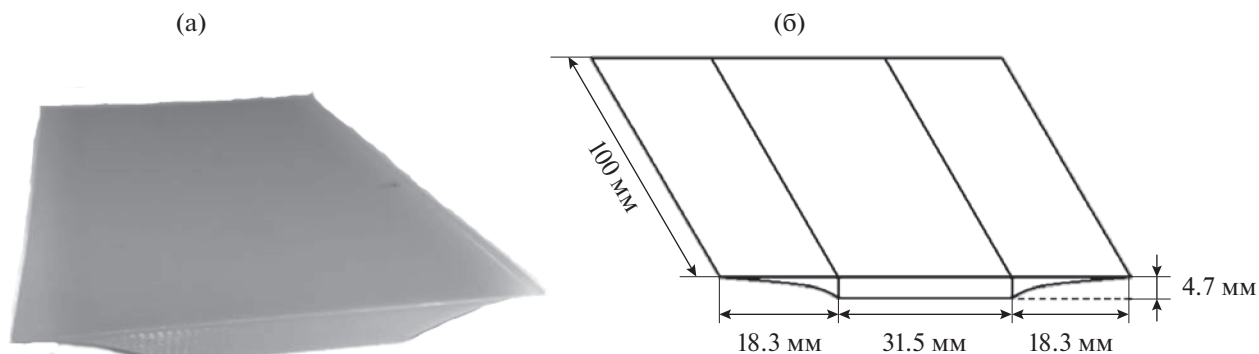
(а) – Фото образца; (б) – размеры образца.
